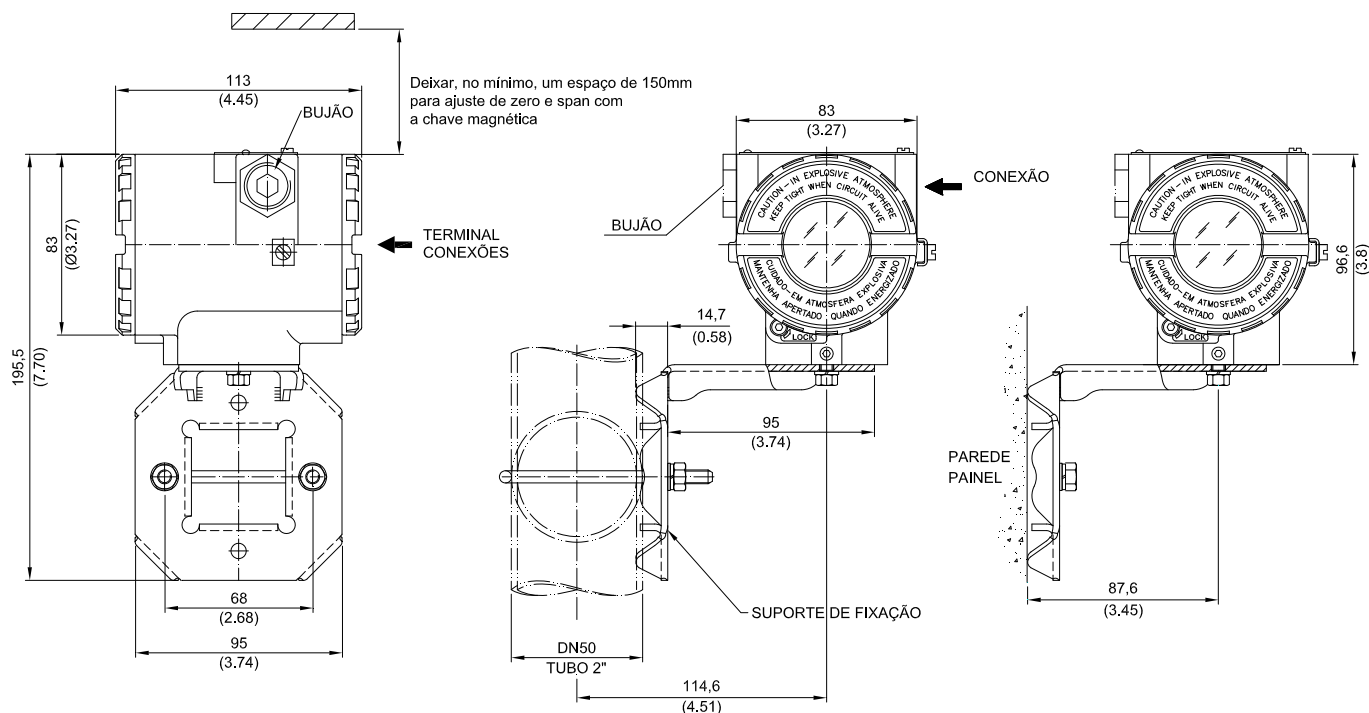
Desenho Dimensional e Posições de Montagem
